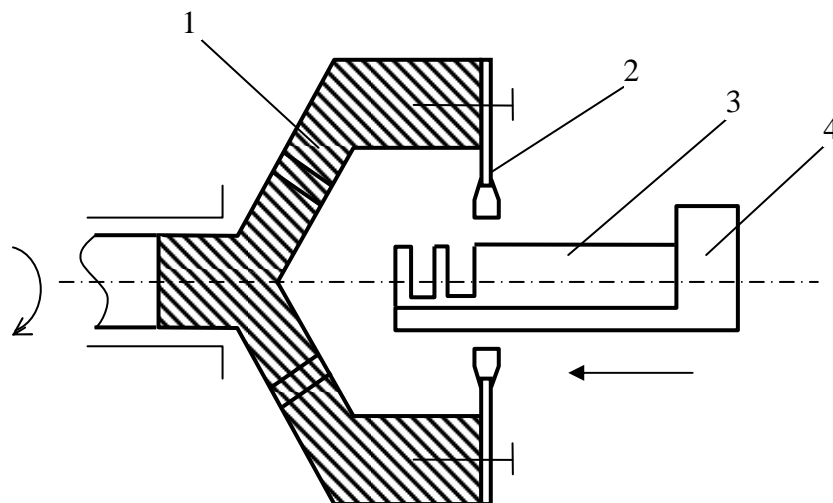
Схема резки слитка на пластины алмазным диском с внутренней режущей кромкой: 1 – шпиндель; 2 – диск с алмазной кромкой; 3 – слиток; 4 – держатель слитка
